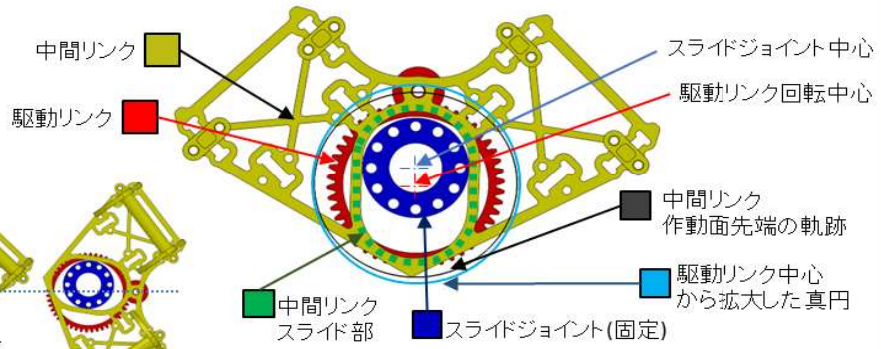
旋回ユニット動作軌跡 平面図(一部断面抜粋)
